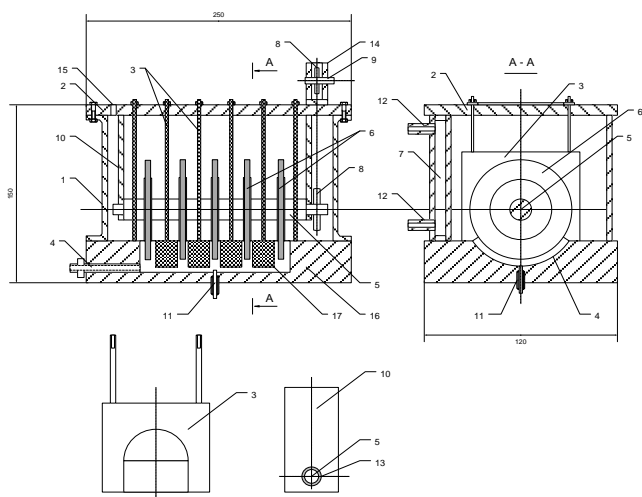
Электролизер с дисковой вращающейся галлированной катодной поверхностью: 1 - корпус электролизера; 2 - крышка; 3 - анод; 4 - катодный токопровод; 5 - катодный вал; 6 - катодный диск; 7 - камера для греющей жидкости; 8 - шкив; 9 - вал для привода; 10 - несущая стойка; 11 - сгон для галлия; 12 - сгон для греющей жидкости; 13 - фторпластовая втулка; 14 - опора для шкива; 15 - отверстие для залива раствора; 16 - днище; 17 - вкладыши
